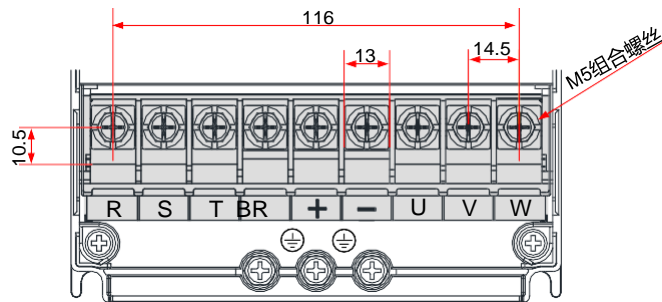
GT600-4T7.5GB/ GT600-4T11GB 三相 380V ~ 480V; GT600-2T5.5GB 三相 200V ~ 240V
